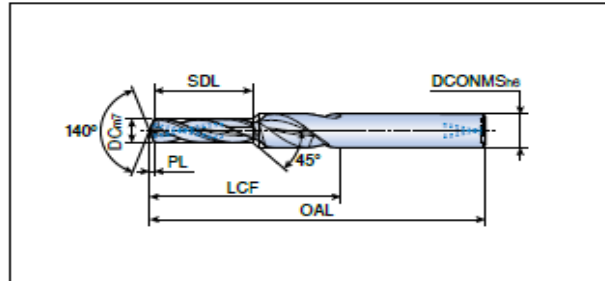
Загальний вигляд та розміри центрувальних свердл
